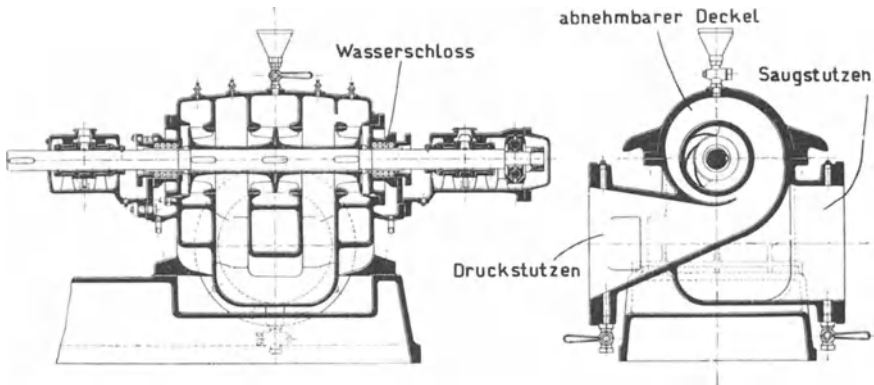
und 345. Raschlaufende Kühlwasserpumpe der Maschinenbau A.-G. Balcke.
